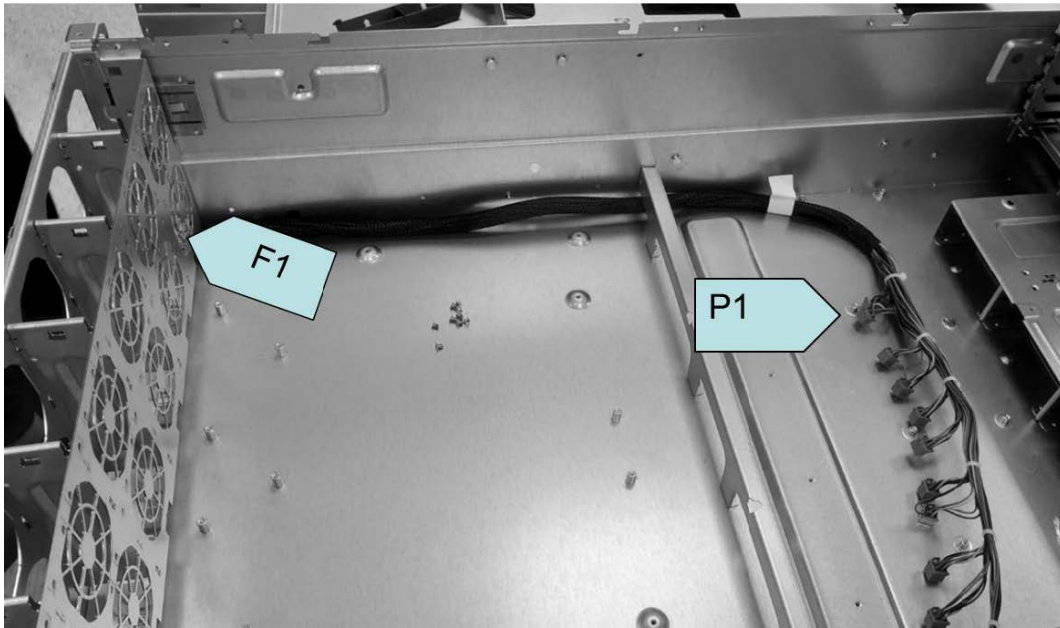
Assemblage du câble de ventilateur vers le support de ventilateur
